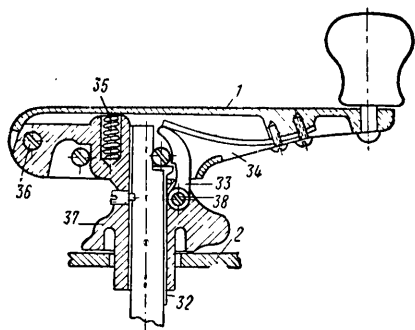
Разрез главной рукоятки контроллера машиниста КВ-6Б:
